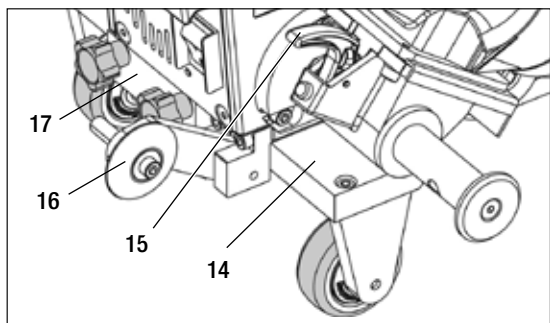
/ Dispositivo di bloccaggio soffiante dell'aria calda (15)
